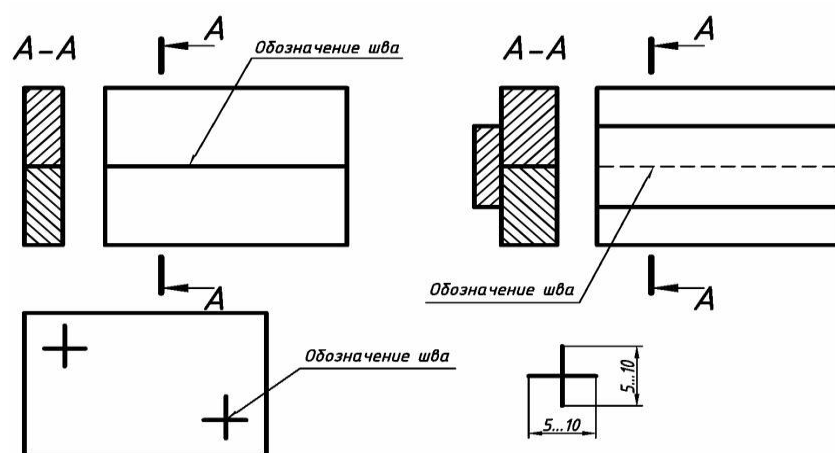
Условное изображение видимых и невидимых сварных швов сварных соединений
